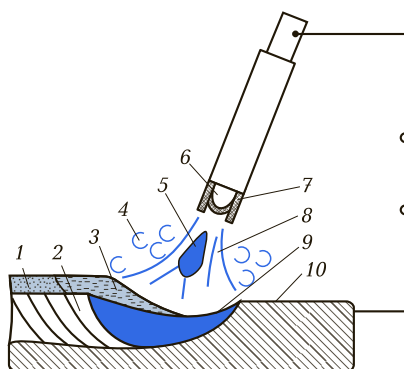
Схема ручной дуговой сварки покрытыми электродами:
